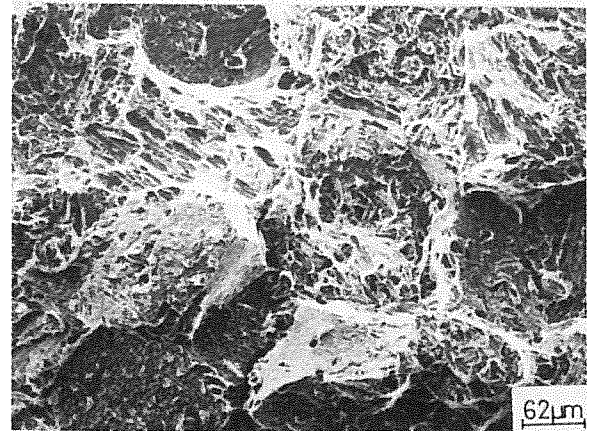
Zona fracturada intergranularmente. Probeta austenizada a 1300°C.
